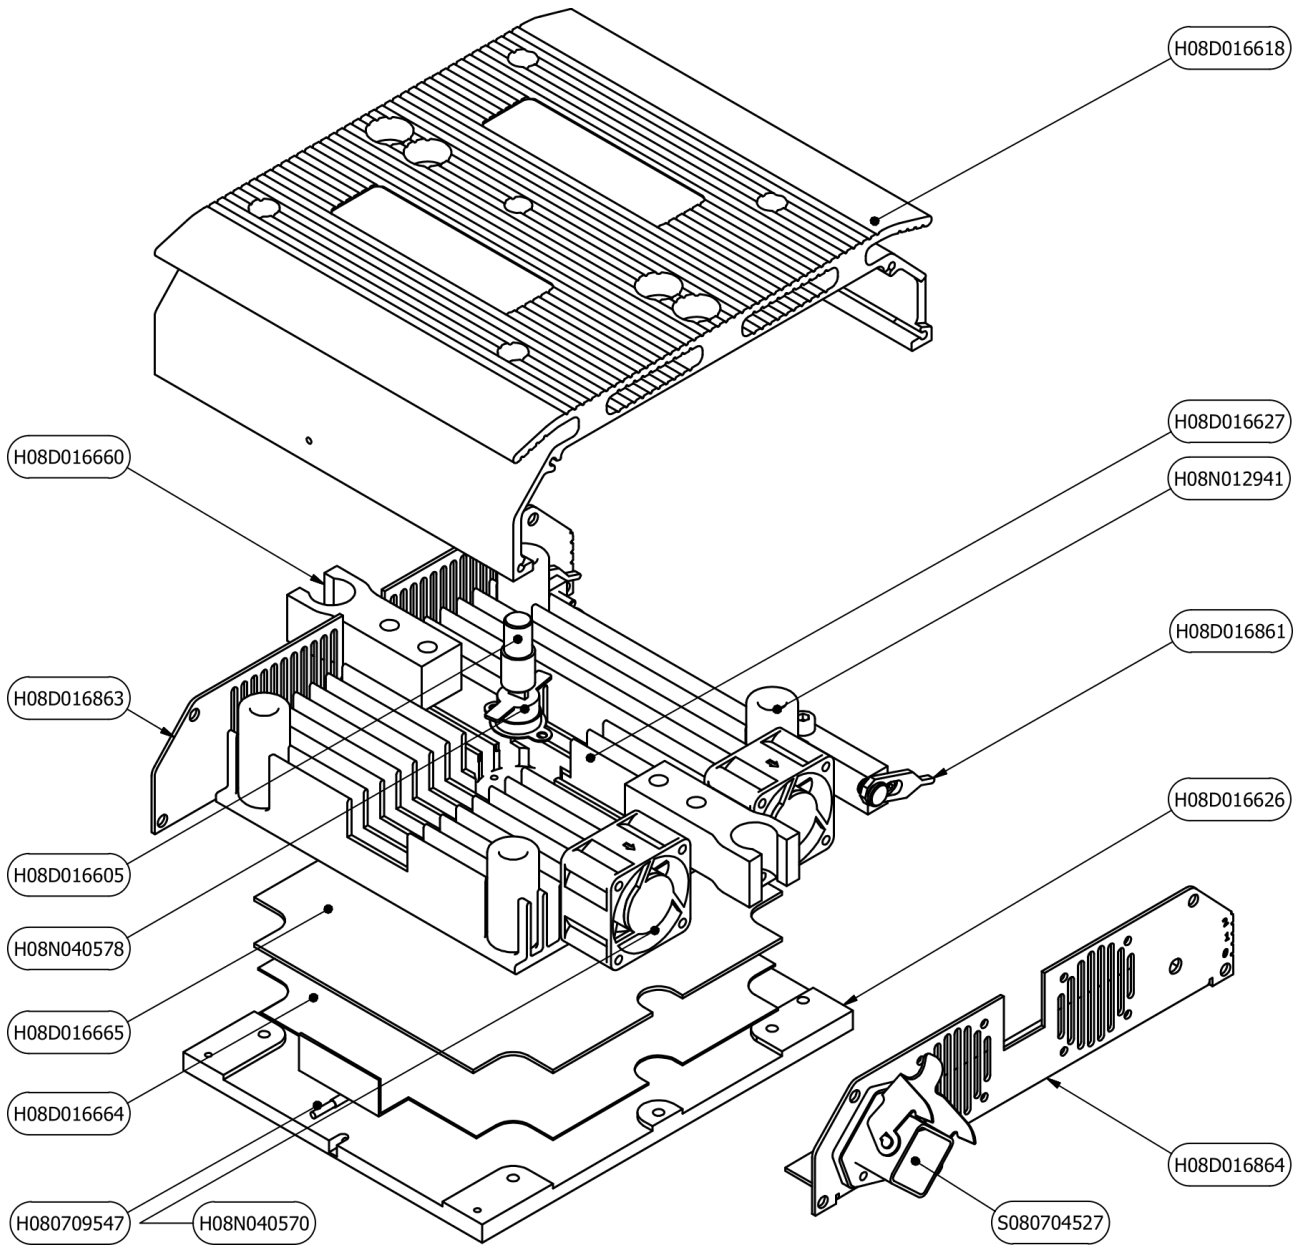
H08D016625 Assemblage de plaque chauffante supérieure PML-100
